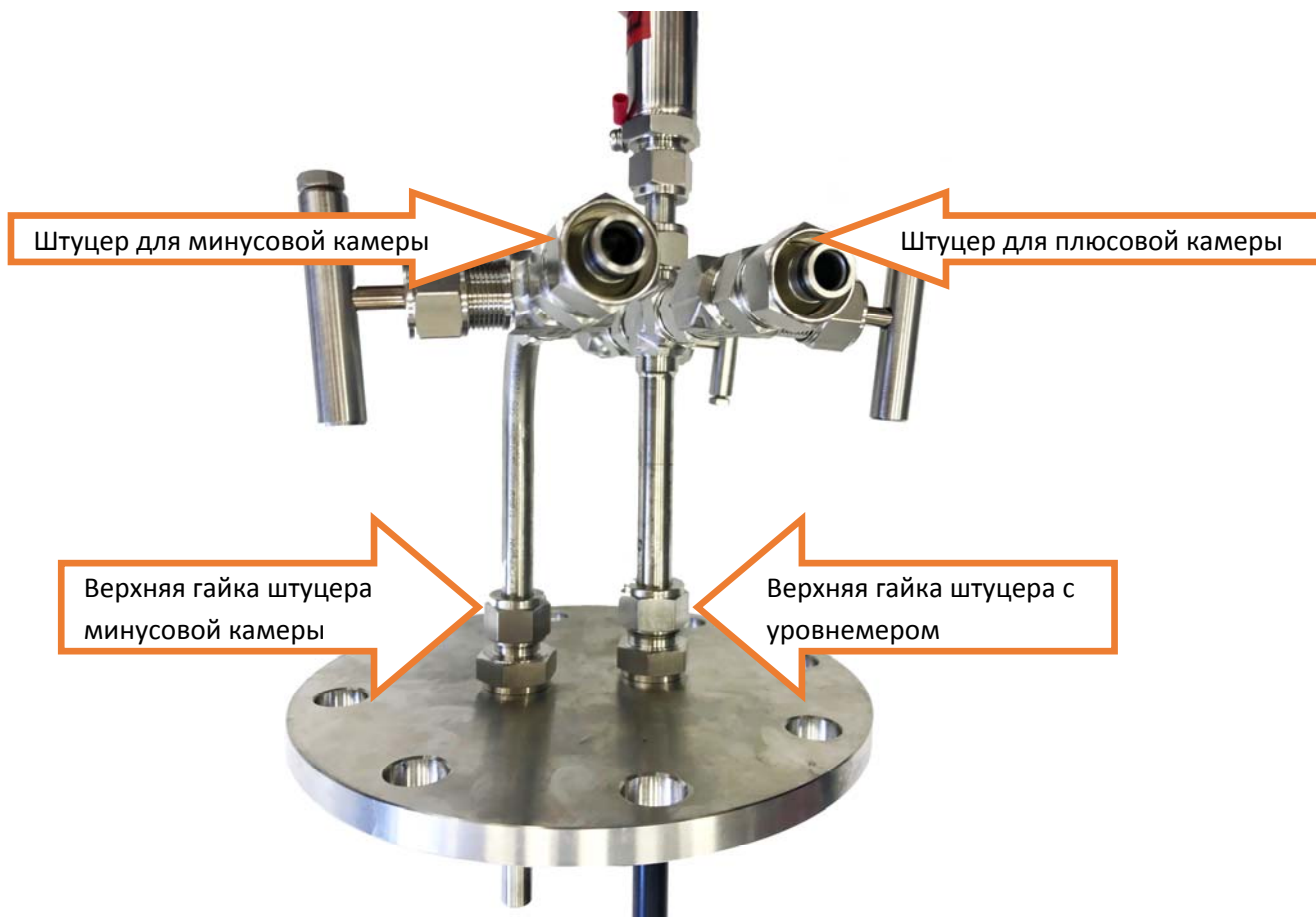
Установка штуцеров для присоединения датчика давления
